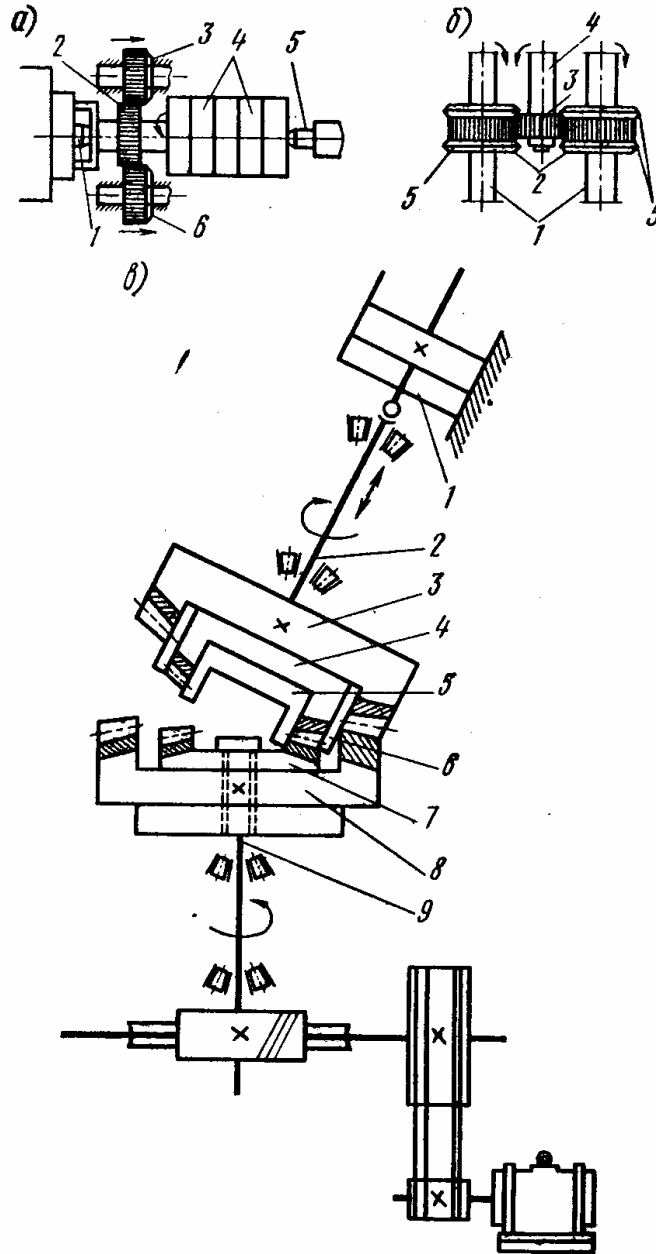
Методы накатывания зубьев зубчатых колес:
